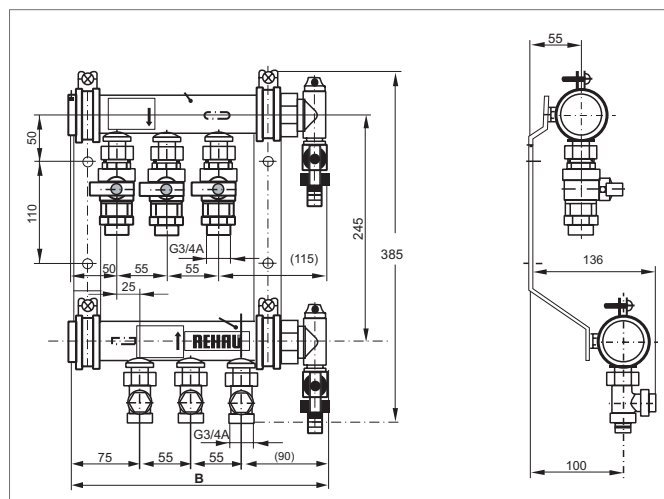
Průmyslový rozdělovač 1¼" IVK
